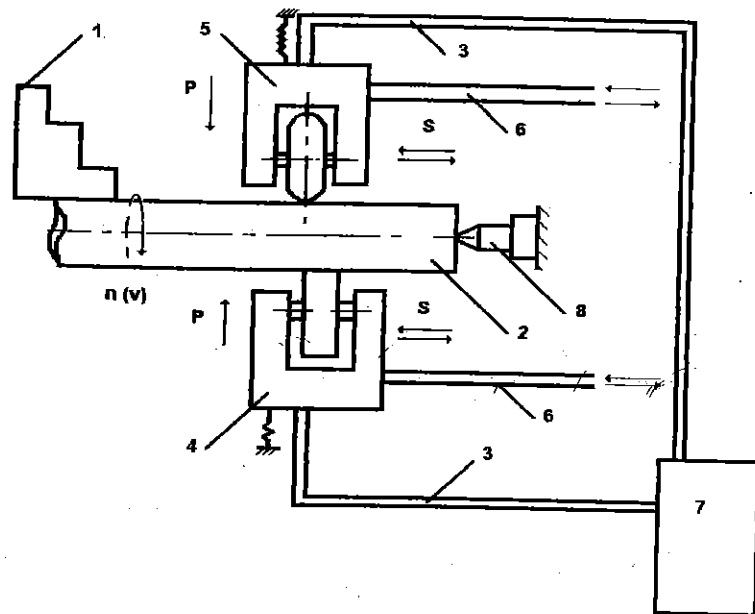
Схема установки для ЛДЭО: 1. токарный патрон; 2. деталь; 3. силовые шины; 4. легирующий инструмент (ролик); 5. выглаживающий инструмент (ролик); 6. охлаждение; 7. источник питания; 8. центр задний.
